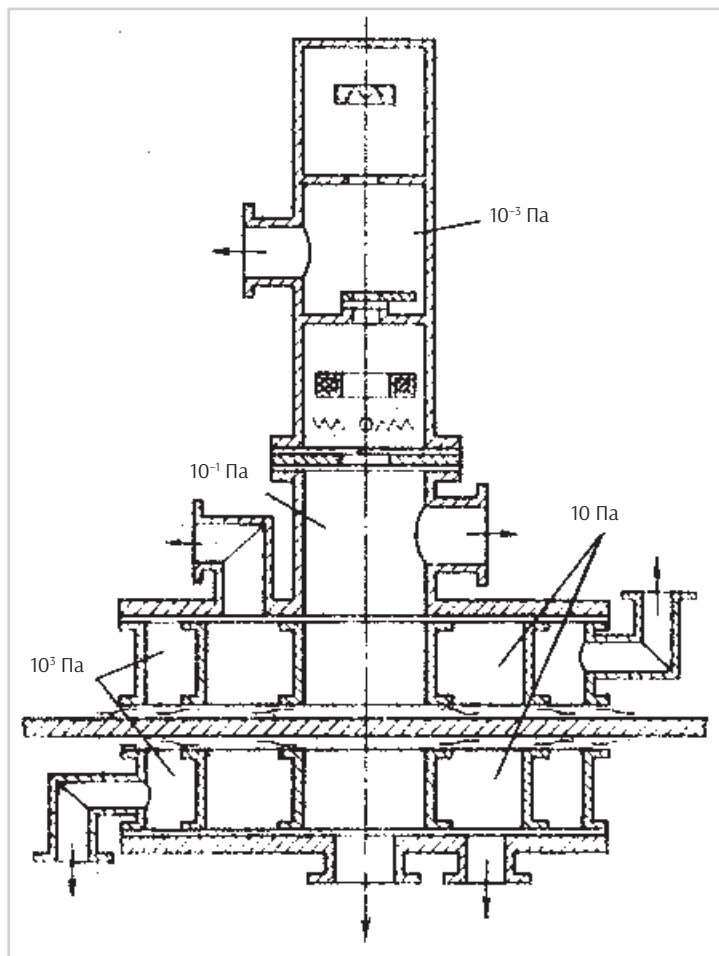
Подвижная установка для электронно-лучевой сварки с частичной герметизацией изделия
